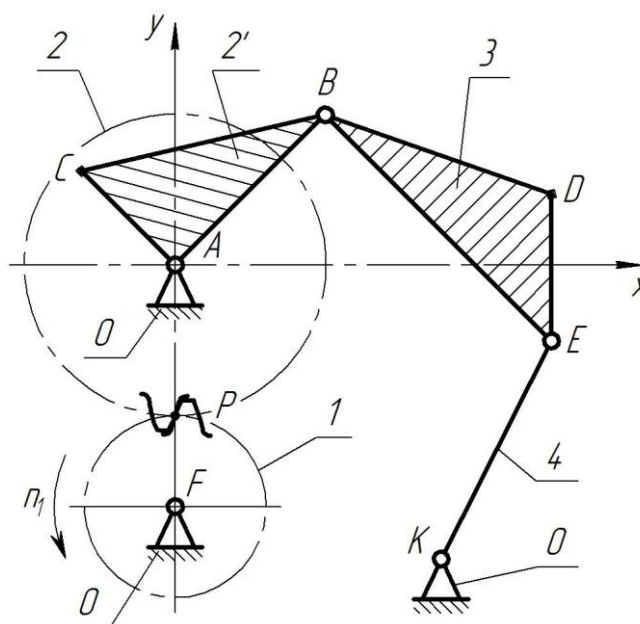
Кинематическая схема зубчато-рычажного механизма
